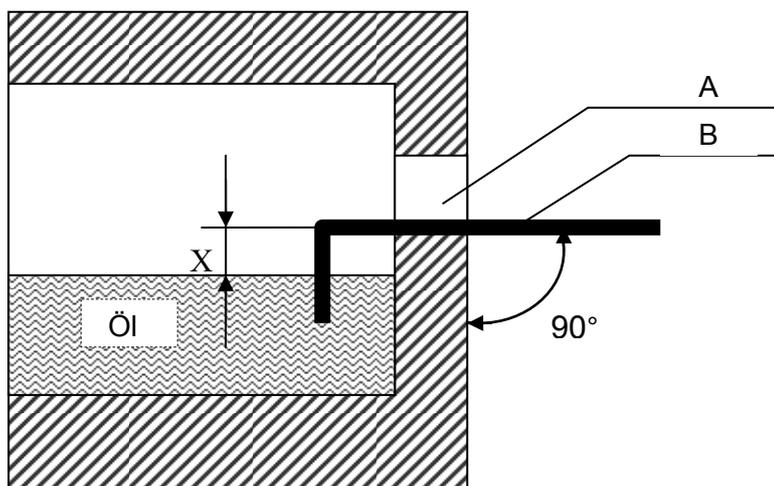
Ölstandskontrolle mit Hilfswerkzeug
